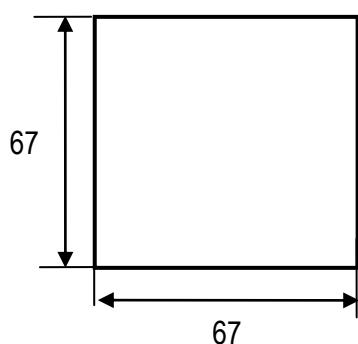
Разметка щита для крепления ИП для конструктивного исполнения М
